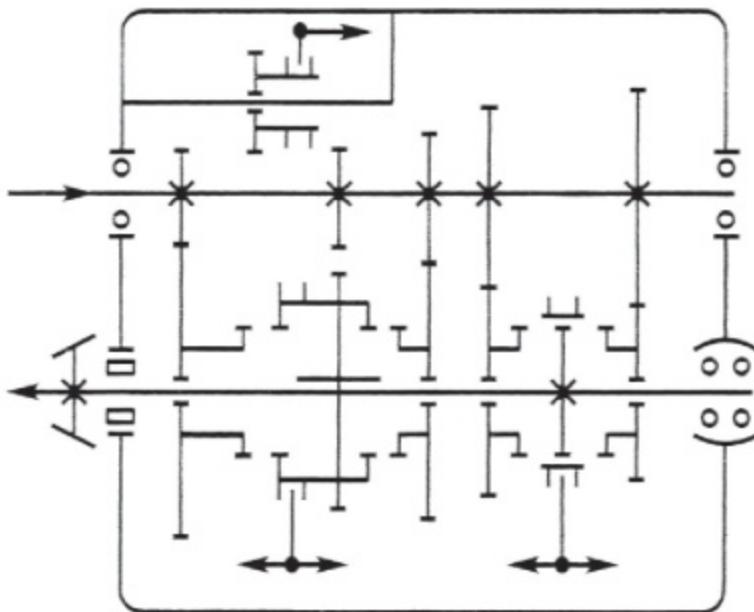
Схема силового агрегата с 3-вальной коробкой передач при расположении ее валов на 3 осях без совмещения и установке главной передачи под двигателем
